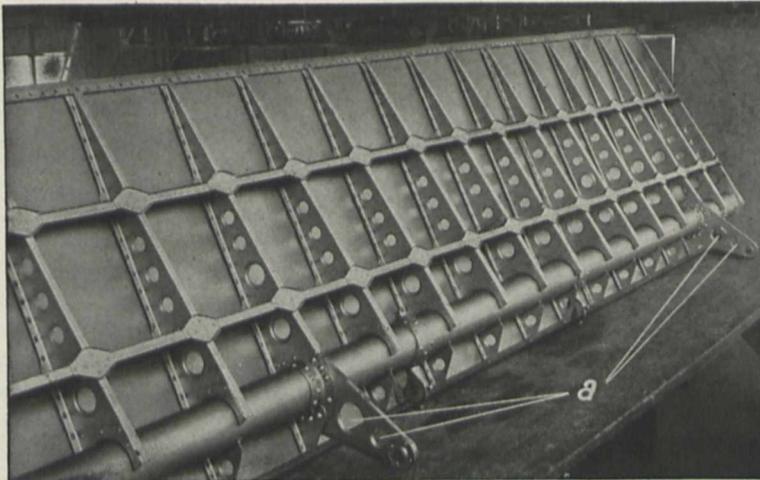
Die Rippen einer Spreizklappe sind mit Durchzügen steif und zugleich leicht gemacht. Auch an den Steuerhebeln sind Bohrungen („a“), die totes Gewicht beheben, deutlich zu erkennen
